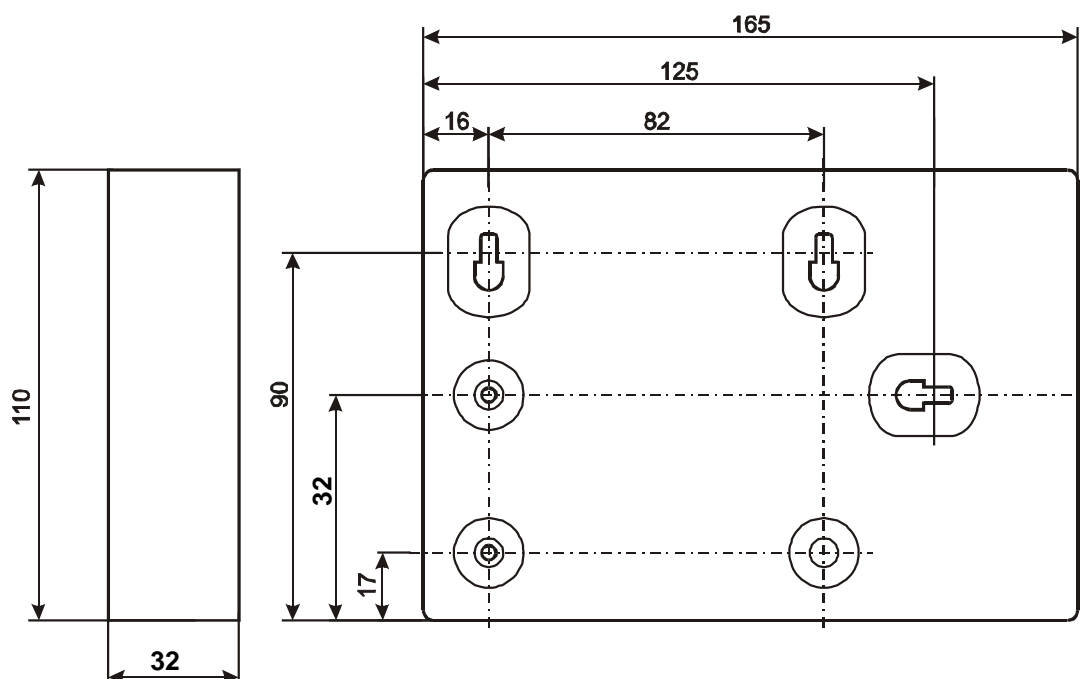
Внешний вид и габаритные размеры СКИУ исп. IP20
